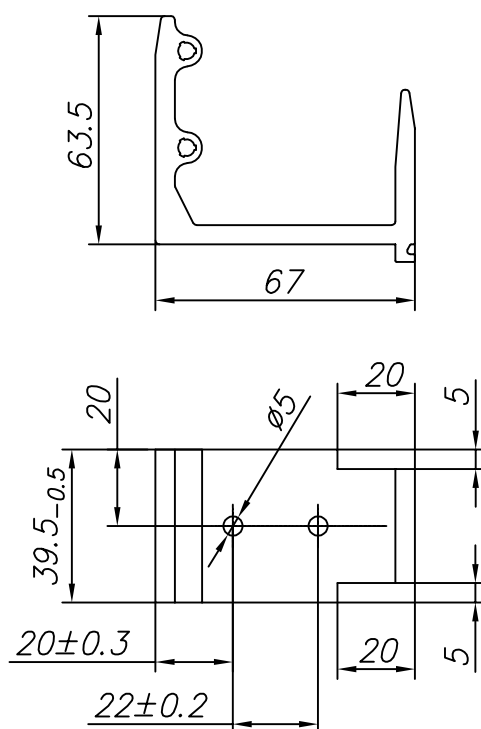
Изготовление соединителя FLGU.400.0912
